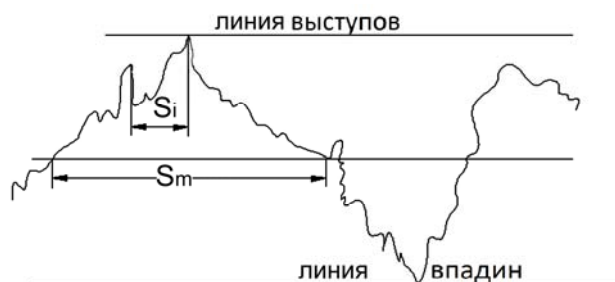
Параметры длины реальной шероховатой поверхности
